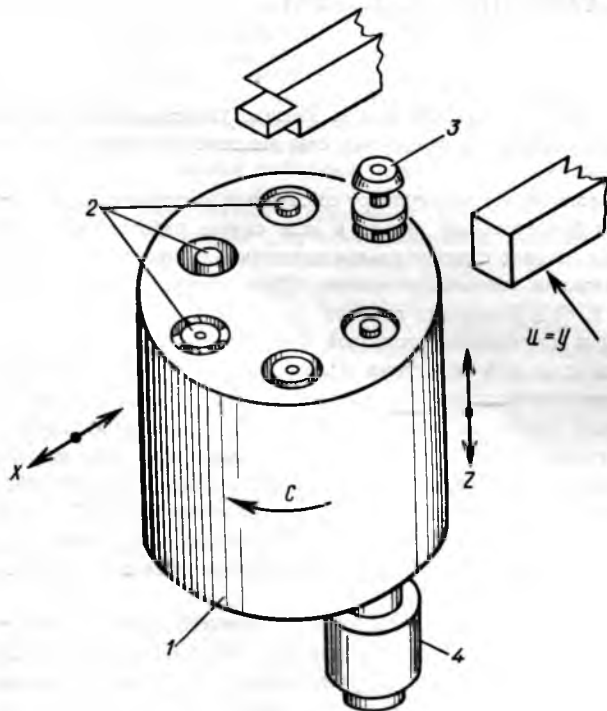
Барабанный инструментальный магазин деревообрабатывающего станка:
